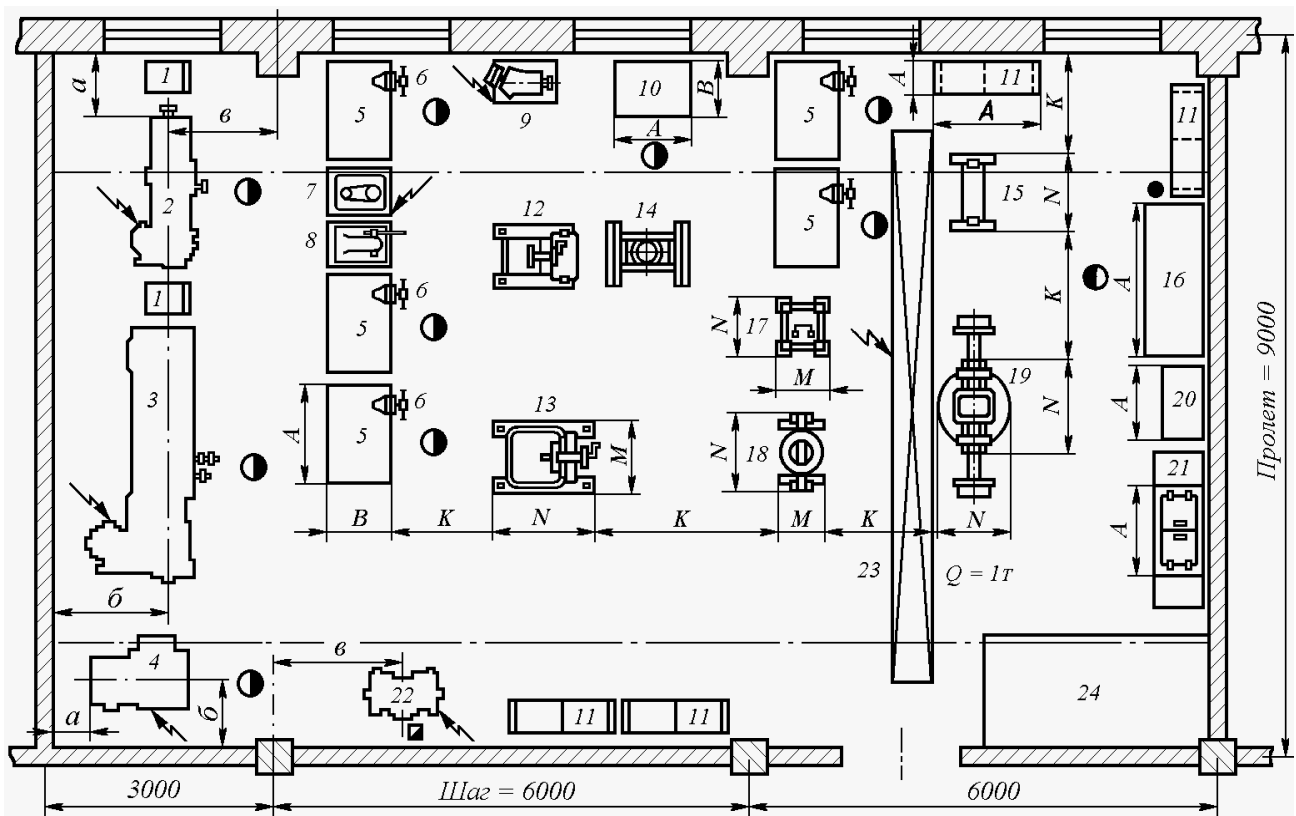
Технологическая планировка агрегатно-механического участка: 1 – инструментальные шкафы; 2 и 3 – токарно-винторезные станки; 4 – сверлильный станок; 5 – слесарные верстаки; 6 – тиски; 7 – настольный сверлильный станок; 8 – пресс с ручным приводом; 9 – илфовальный станок; 10 – поворачивающая плита; 11 – стеллаж для деталей; 12 и 13 – стенды для ремонта основных и пусковых двигателей; 14 – гидравлический пресс; 15 – стенд для ремонта рулевых управлений и карданных валов; 16 – стол для контроля и сортировки деталей; 17 – стенд для ремонта коробок передач; 18 – стенд для ремонта редукторов и задних мостов; 19 – стенд для ремонта передних мостов; 20 – ларь; 21 – ванная для мойки деталей; 22 – заточный станок; 23 – кран-балка; 24 – площадка для агрегатов
